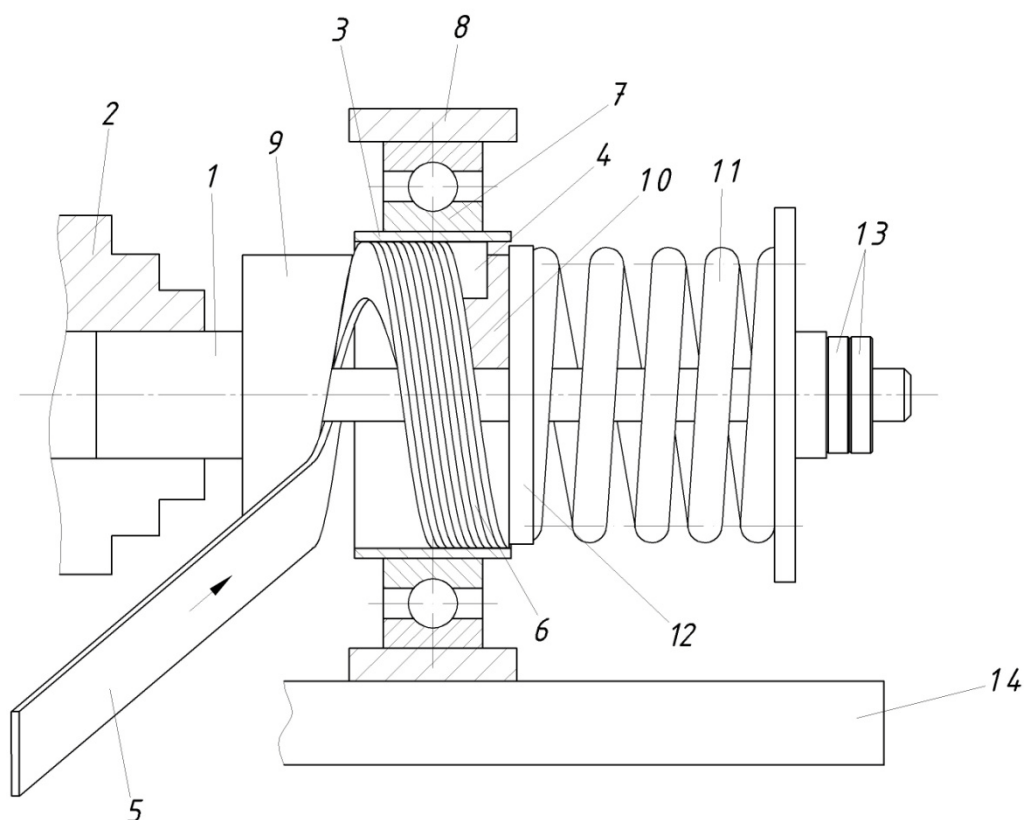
Пристрій для навивання гвинтових спіралей обертовою втулкою
